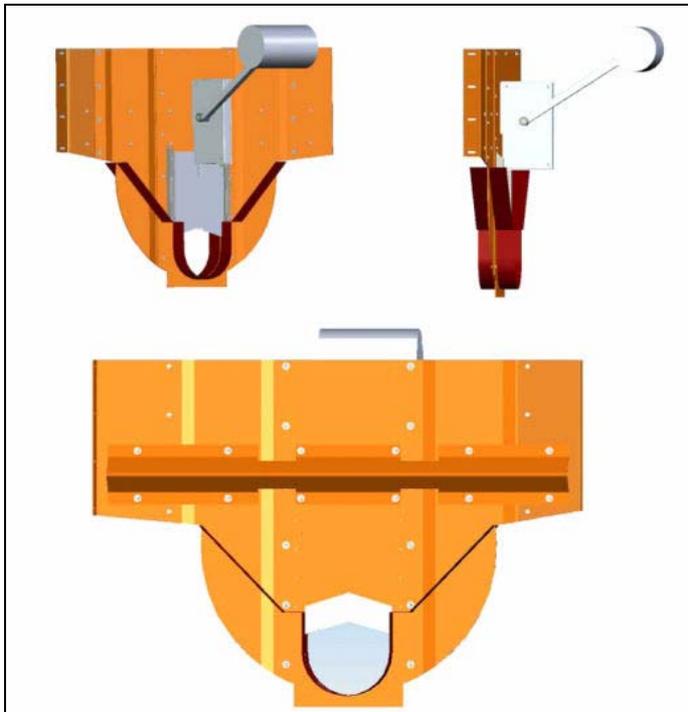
HydrOstyx®-Abflussbremse® mit oberwassergesteuertem Grundablass in Stuttgart
